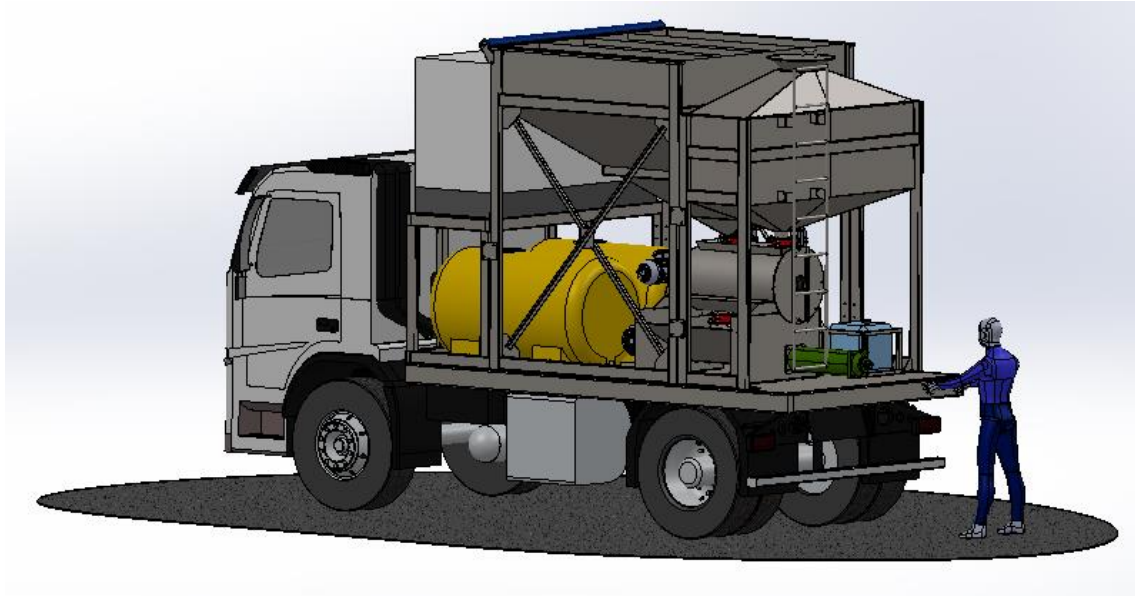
vista del diseño final de la planta móvil. SolidWorks.
